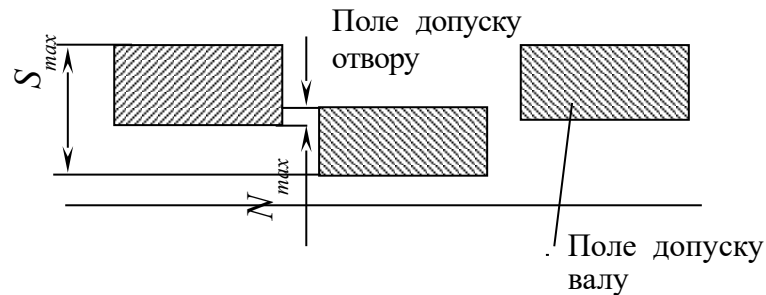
Поля допусків перехідної посадки
